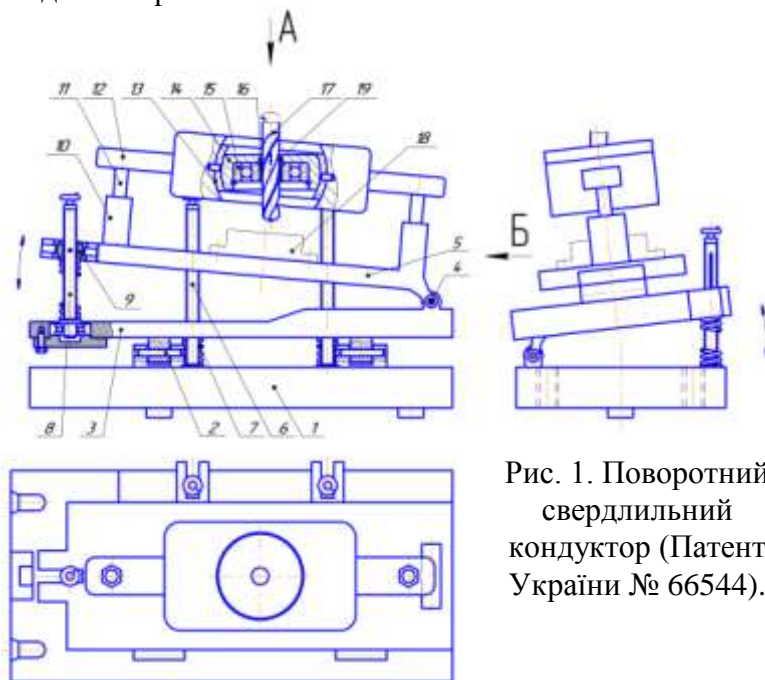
Поворотний свердлильний кондуктор (Патент України № 66544).
